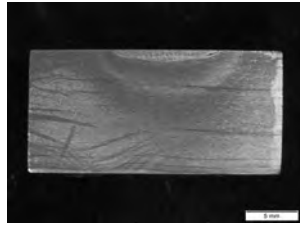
Grundwerkstoff mit Wärmeinflusszone, Schliff, Foto: SLV Halle
